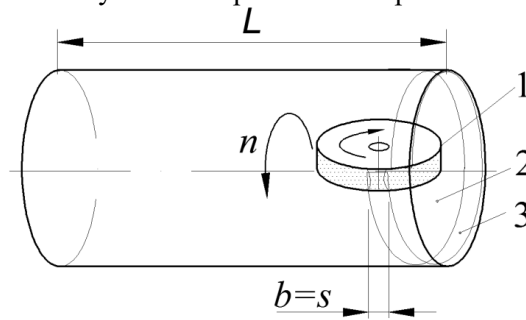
Схема обработки отверстия цилиндра абразивным инструментом: 1 – войлочный круг с наклеенным абразивным порошком; 2- обрабатываемый цилиндр; 3 – шлифованная полоса; b – ширина пятна контакта; s – подача; n – частота вращения детали; L – длина детали
